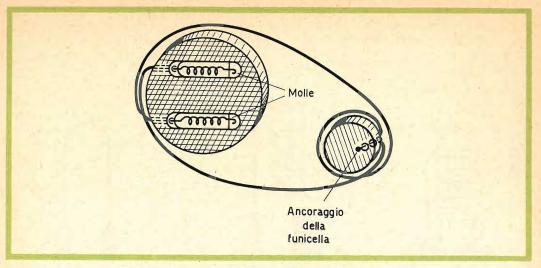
Montaggio e fissaggio del cavo di trascinamento.
